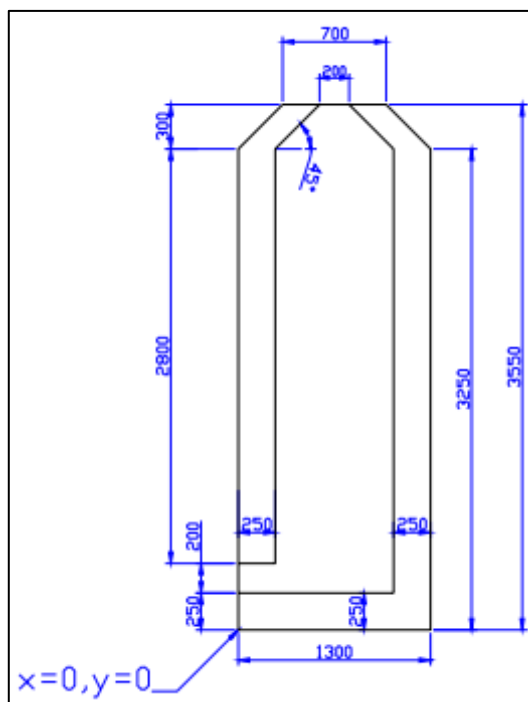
Estrutura e Dimensões do Combustor (AUTORES)
